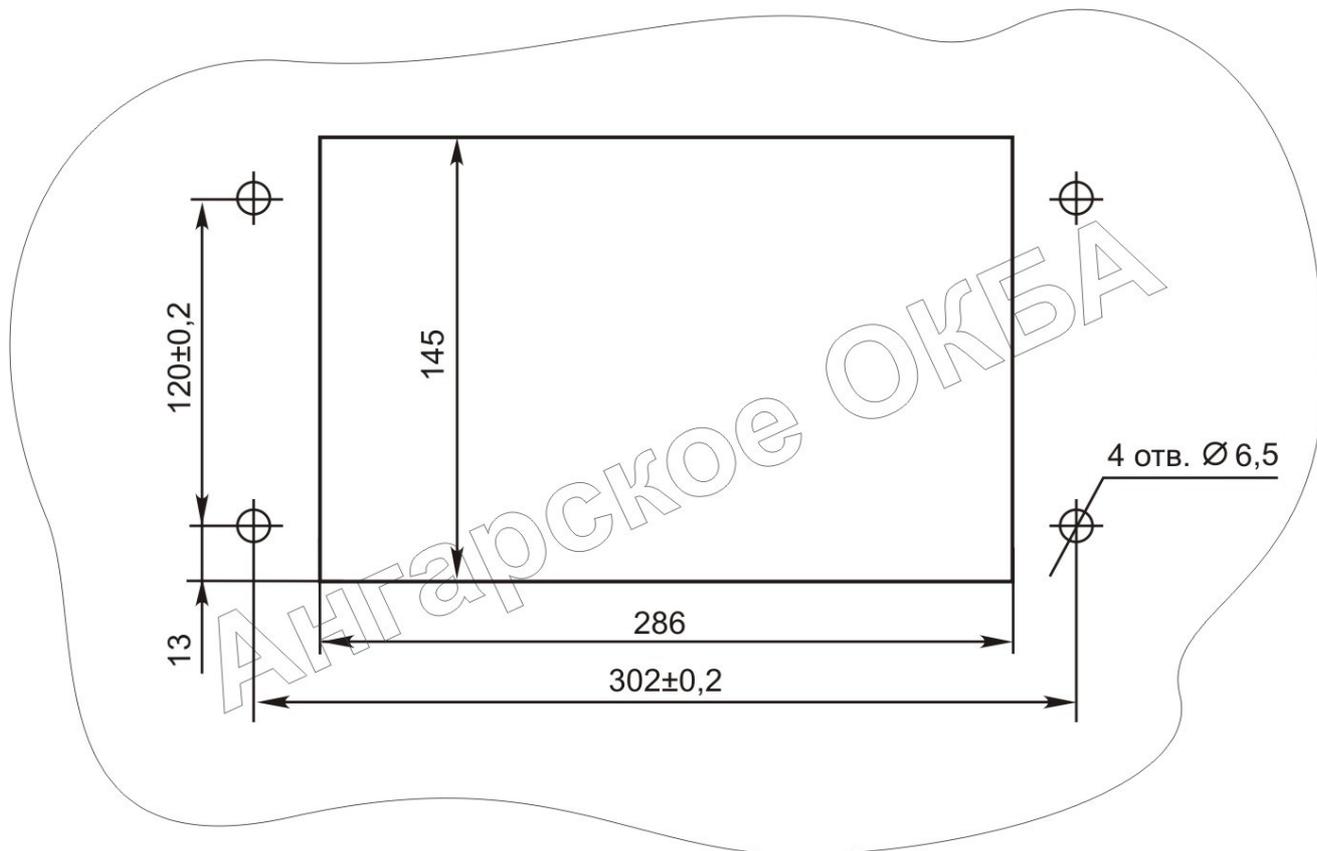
Разметка под крепление газоанализатора на щите.
